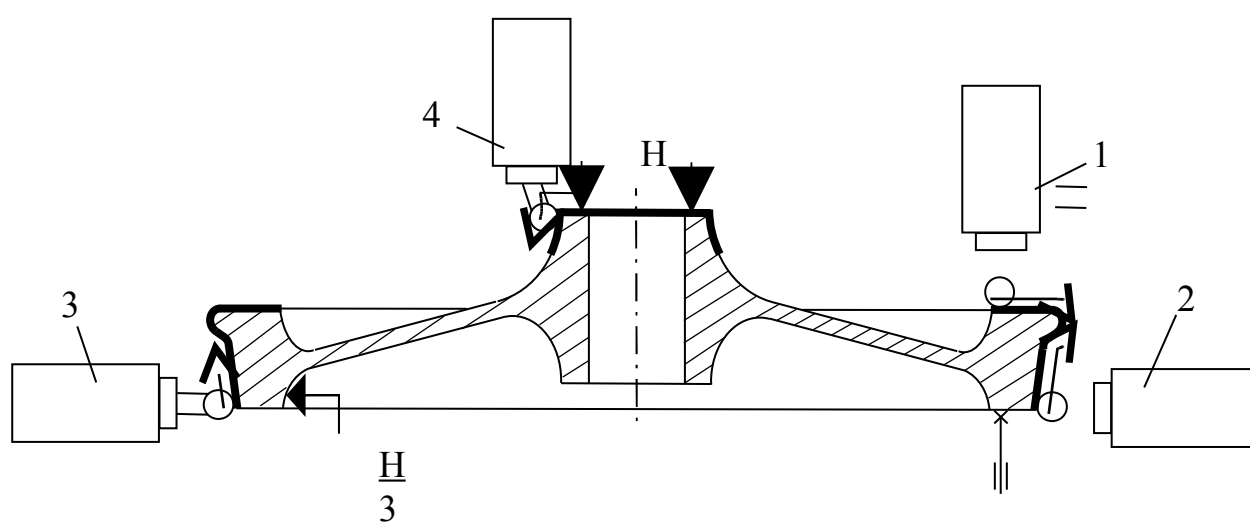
Схема обробки коліс на верстатах моделі 1Б502С и 1В502 при базуванні й закріпленні колеса "гребенем вверх"
